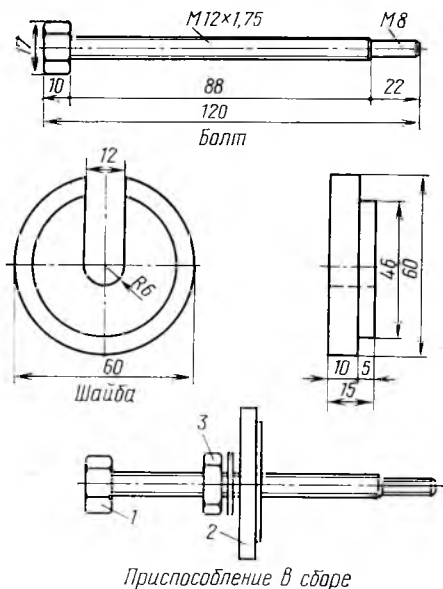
Приспособление для сборки пильного узла станка фирмы «Антон»
